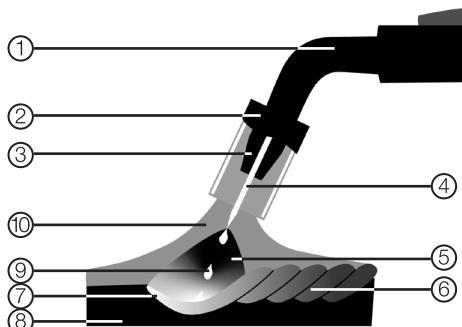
Полуавтоматическая сварка MIG / MAG.
